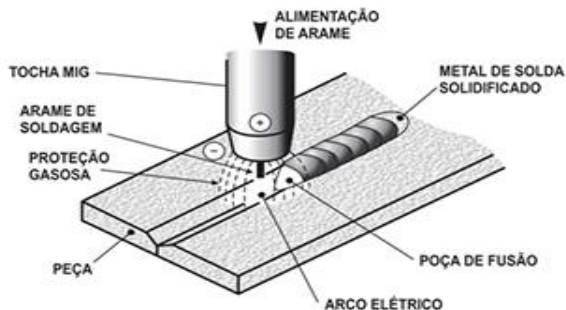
Processo de soldadura MIG/MAG³⁰
